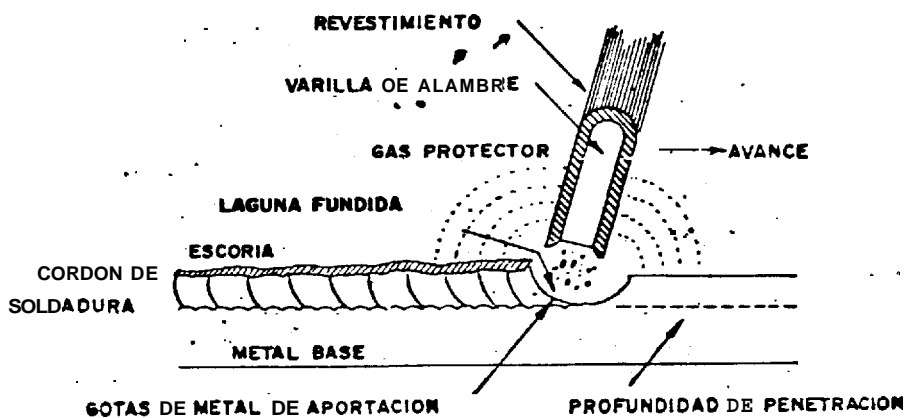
SOLDADURA POR ARCO ELECTRICO (REF. AWS WELDING - HANDBOOK) (Ref. 7)
